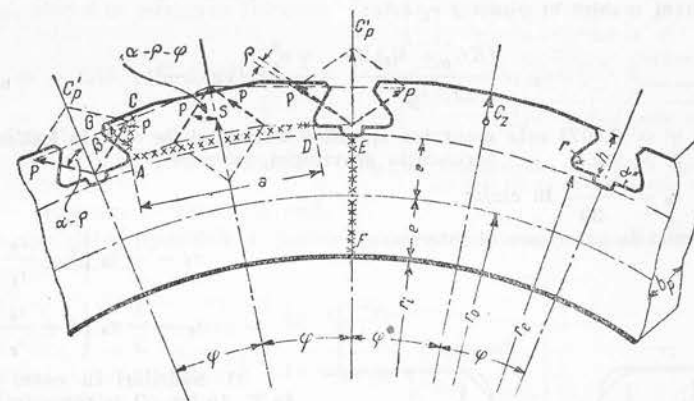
Dimensionarea jugului rotorului și cozilor de rândunică.
